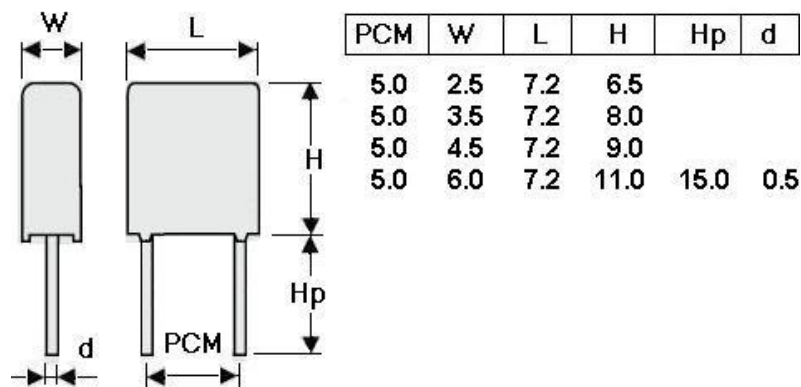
Габаритні розміри конденсатора В32529С1102J000
